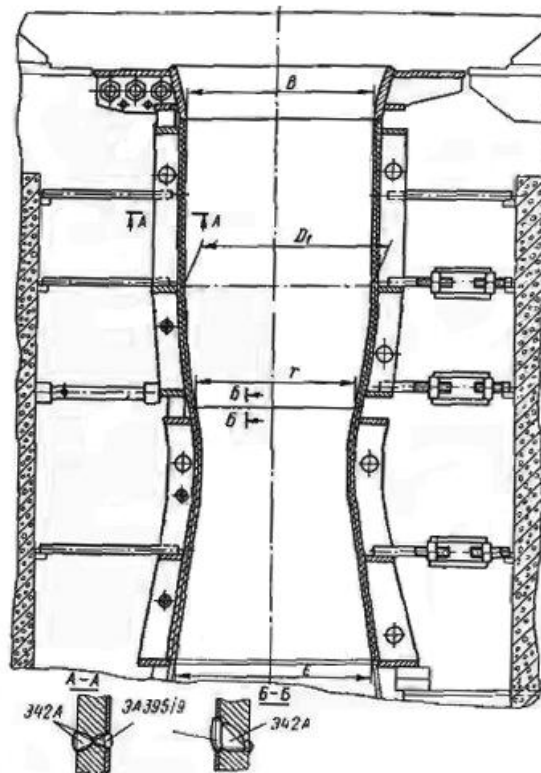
Камера рабочего колеса и конус отсасывающей трубы поворотно-лопастной турбины
